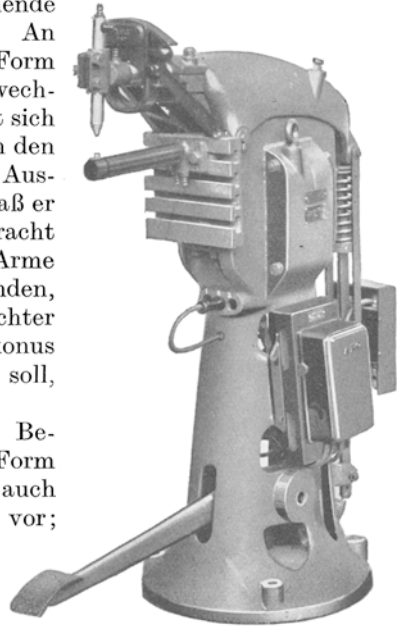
Normale Punktschweißmaschine mit Schweißkontroller.
